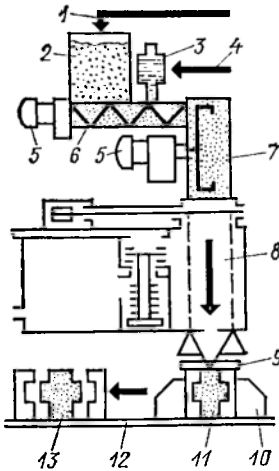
Схема изготовления стержней из быстро-самотвердеющих смесей (БХТС):
